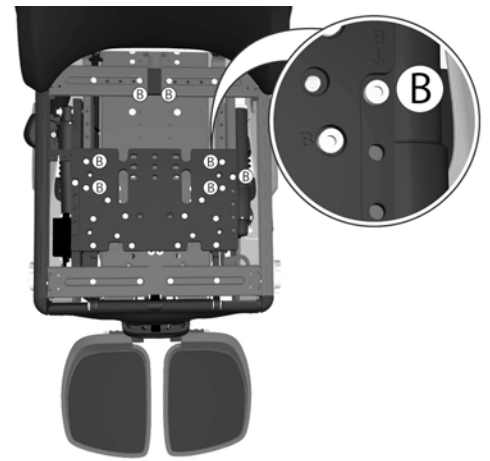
Die Position des hinteren Abschnitts des Sitzrahmens (Rückenlehnenposition) ist mit fünf Schrauben befestigt, die hier mit dem Buchstaben B markiert sind.
